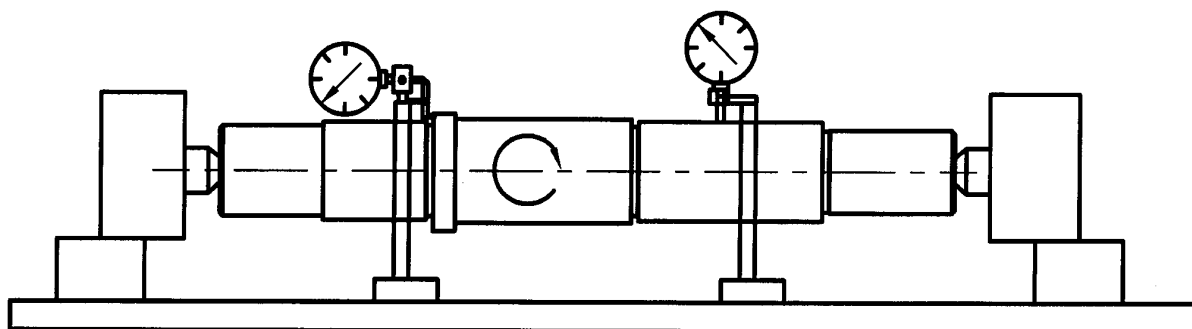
Схема контроля радиального и торцового биения вала
